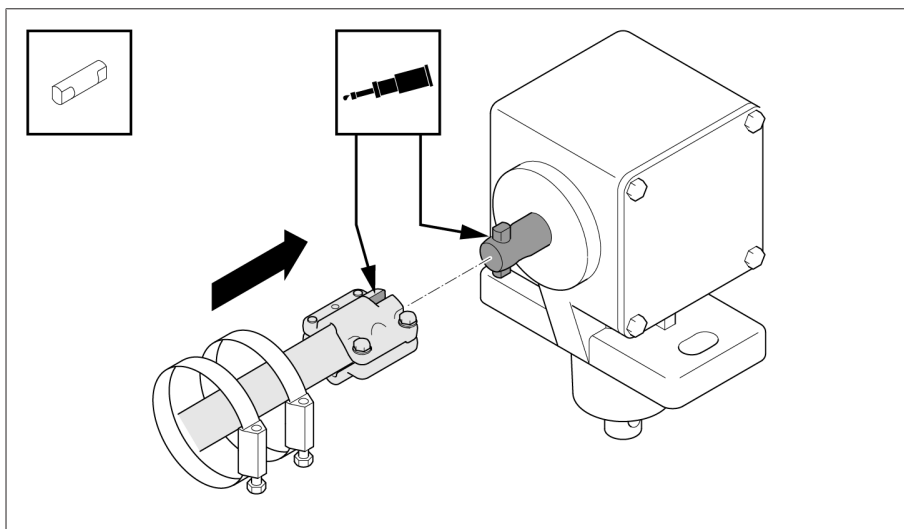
Glissez le tube carré avec la pièce d'accouplement sur l'extrémité d'arbre
